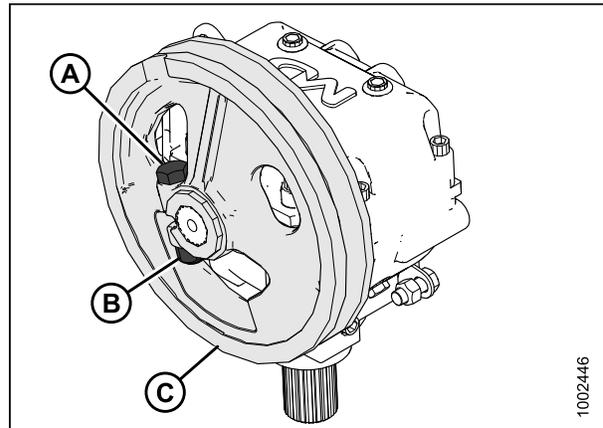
Редуктор привода ножа (МКШ) и шкив
